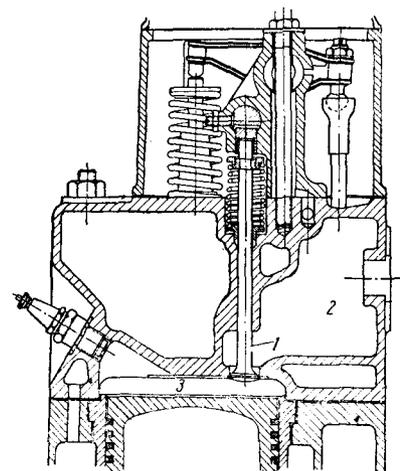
Головка двигателя трактора ХТЗ-НАТИ-Т2Г:
